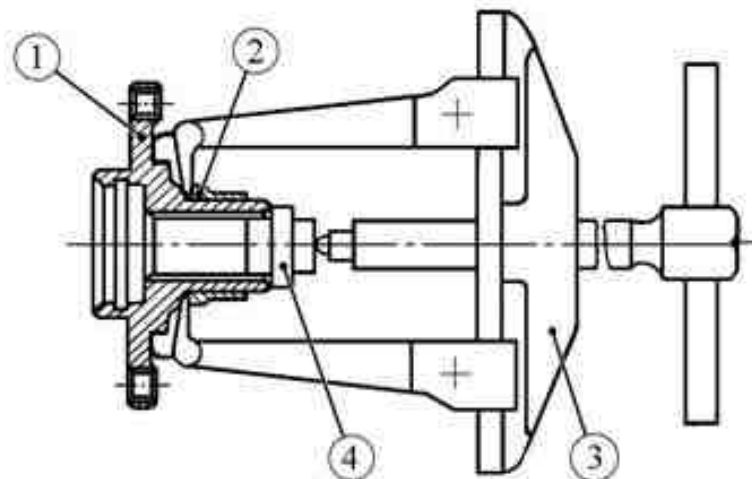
Спрессовка внутреннего кольца подшипника со ступицы переднего колеса:
